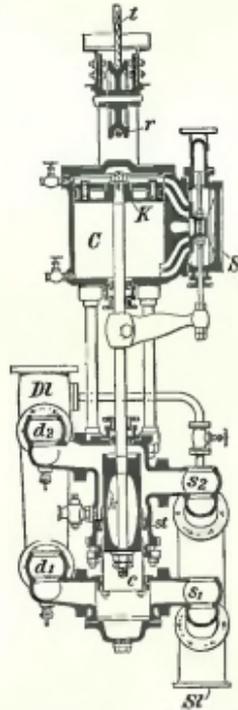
Schnitt durch eine Hälfte einer Duplexpumpe für Abteufzwecke.
